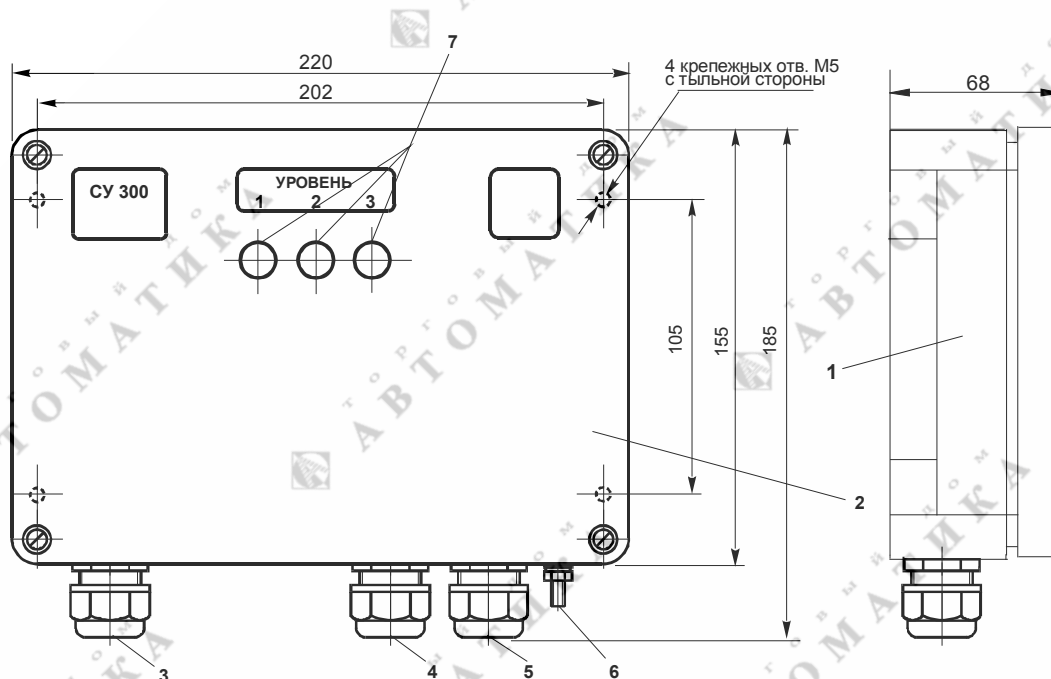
Внешний вид и габаритные размеры вторичного преобразователя
